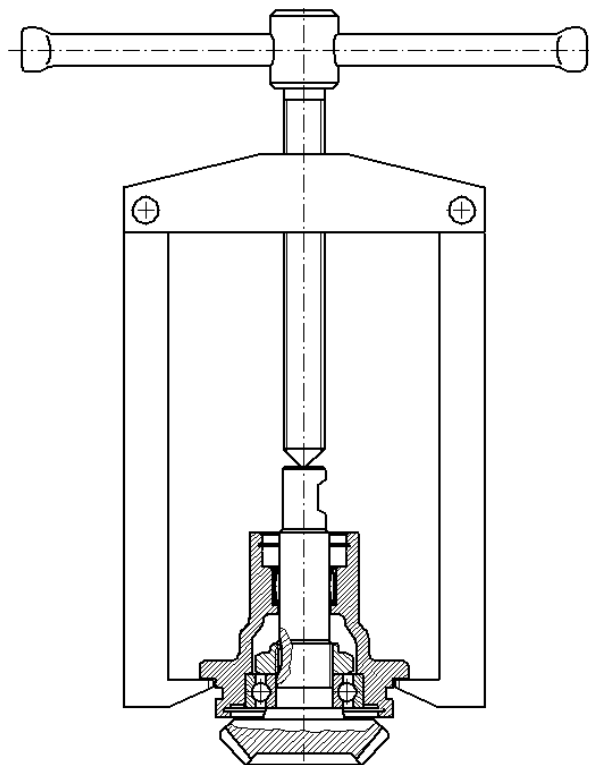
Здійснюється видалення ведучої шестерні та підшипника із корпусу шляхом випресовування.
